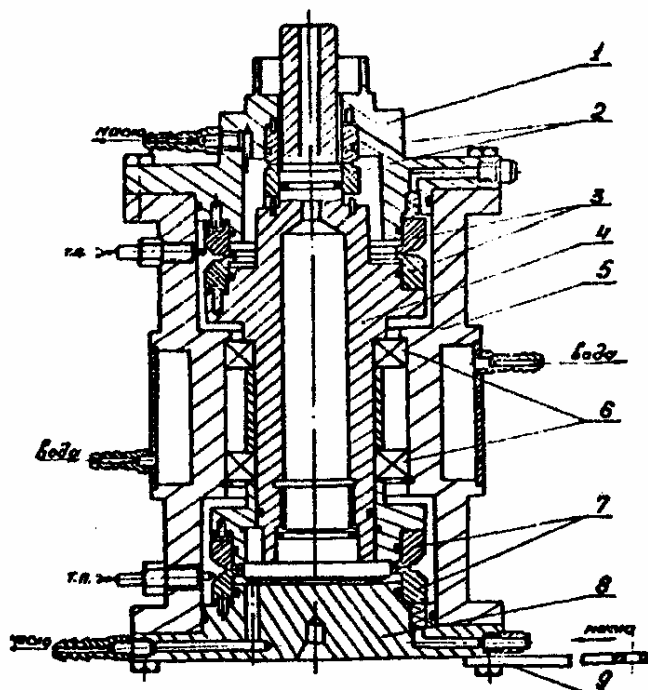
Рабочий узел стенда для испытания торцовых уплотнений: 1 — верхняя крышка; 2 — запирающее торцовое уплотнение; 3 — верхнее торцовое уплотнение; 4 — вал; 5 — корпус; 6 — шарикоподшипник; 7 — нижнее торцовое уплотнение; 8 — нижняя крышка; 9 — рычаг.
